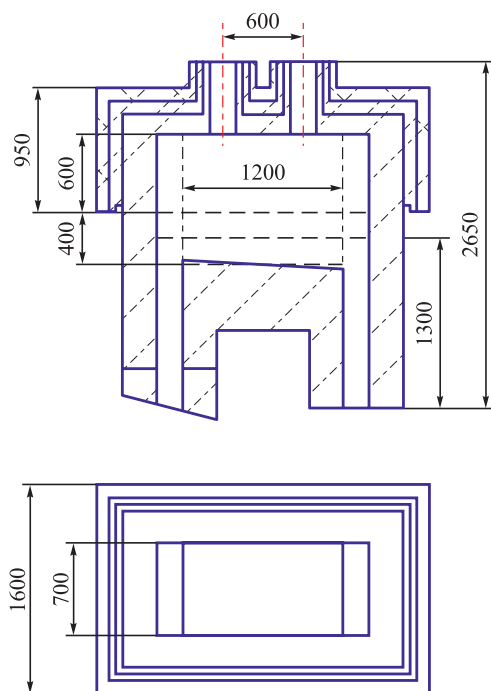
Эскизный чертеж вакуум-камеры (разрез сбоку и вид снизу)
